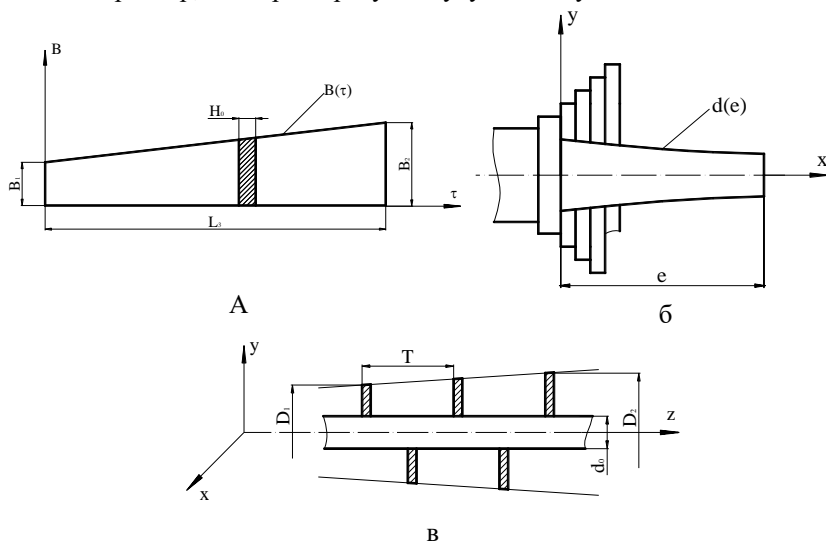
Розрахункова схема для проектування конічних робочих органів [4]: а - заготовка спіралі конічного шнека; б - схема навивання конічної трапецеподібної заготовки в пакет; в - конструкція конічного шнека
